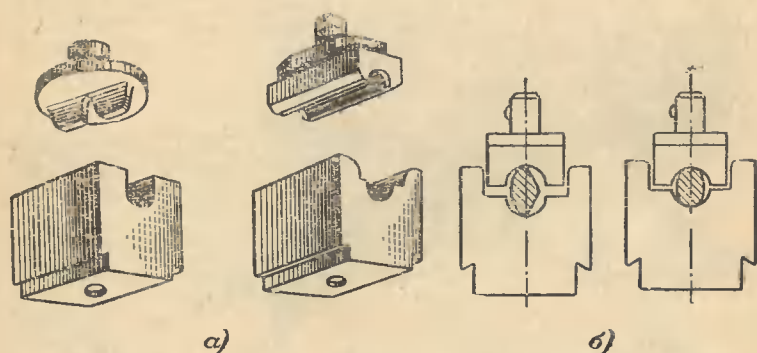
Набор инструментов для опрессовки алюминиевых наконечников.
